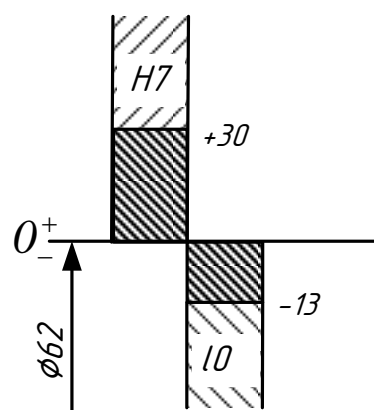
Схема полей посадки наружного кольца подшипника с отверстием в корпусе
